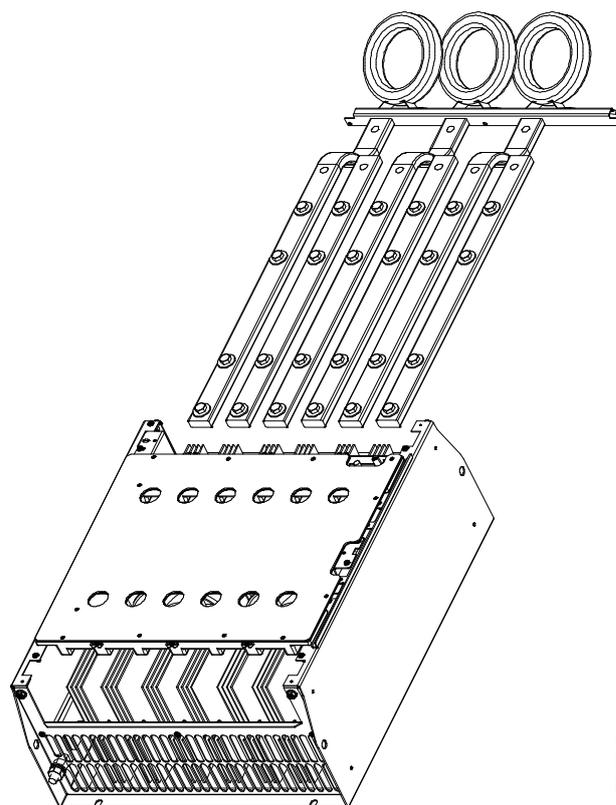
Barras condutoras com braçadeiras para cabos
